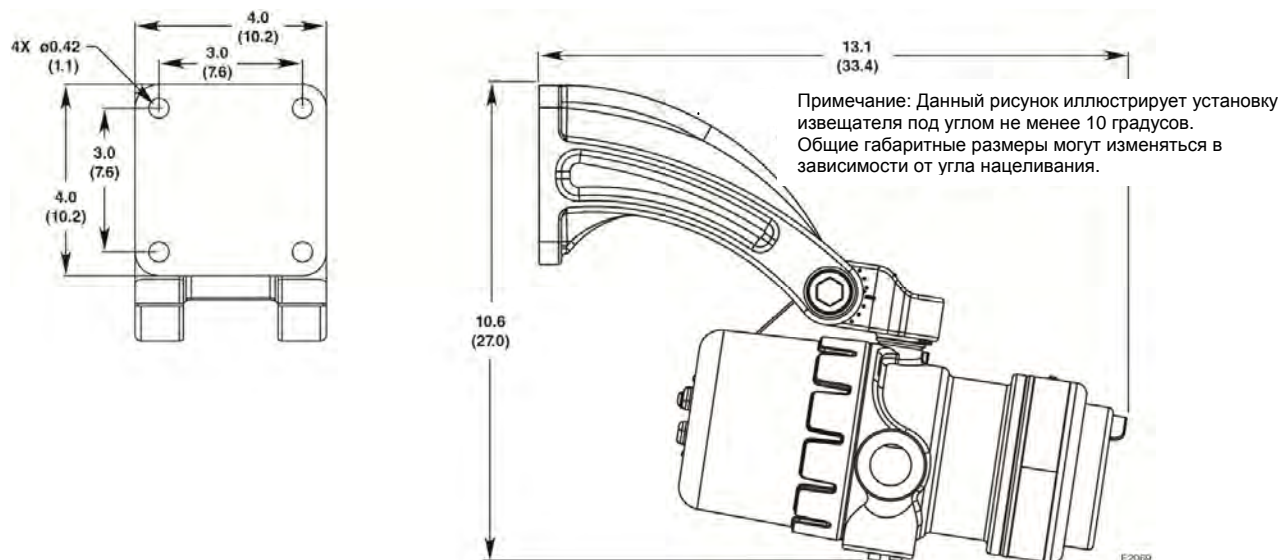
Габаритные размеры извещателя с монтажным кронштейном Q9033 в дюймах (см).
